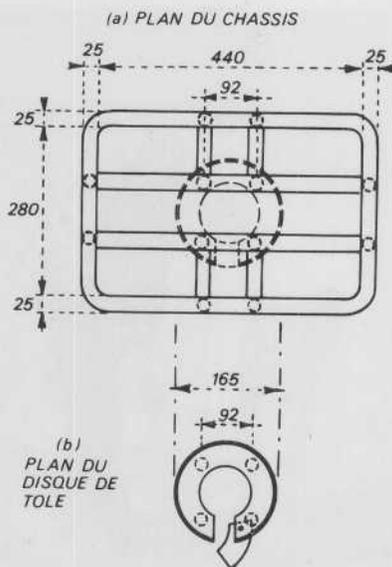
(a) LE CHASSIS METALLIQUE ET (b) LE DISQUE DE TOLE
